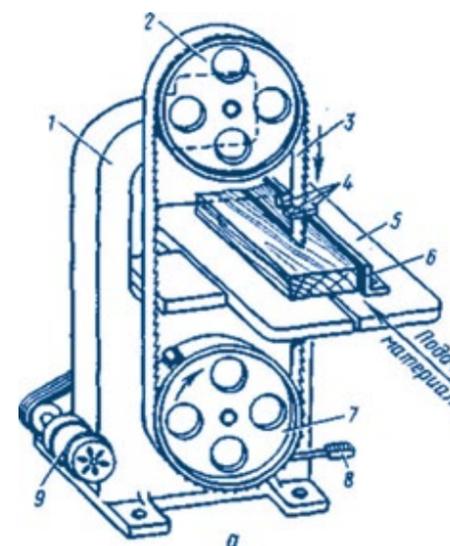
Столярный ленточно-пильный станок с ручной подачей: 1 – станина; 2 – верхний неприводной шкив; 3 – пила; 4 – направляющее устройство; 5 – рабочий стол; 6 – направляющая линейка; 7 – приводной шкив; 8 – педаль тормоза; 9 – электродвигатель; 10 – щетка
